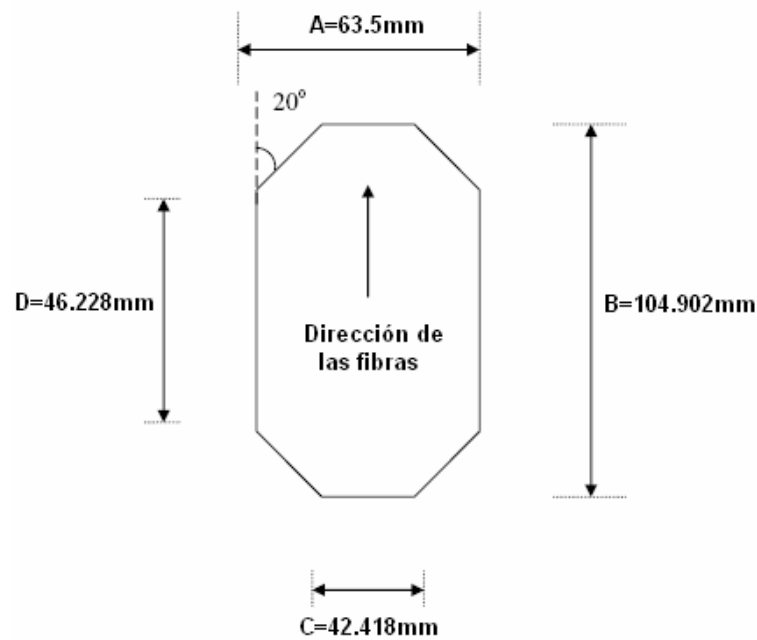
Dimensiones de la primer capa sobre el panel de aluminio [6].
